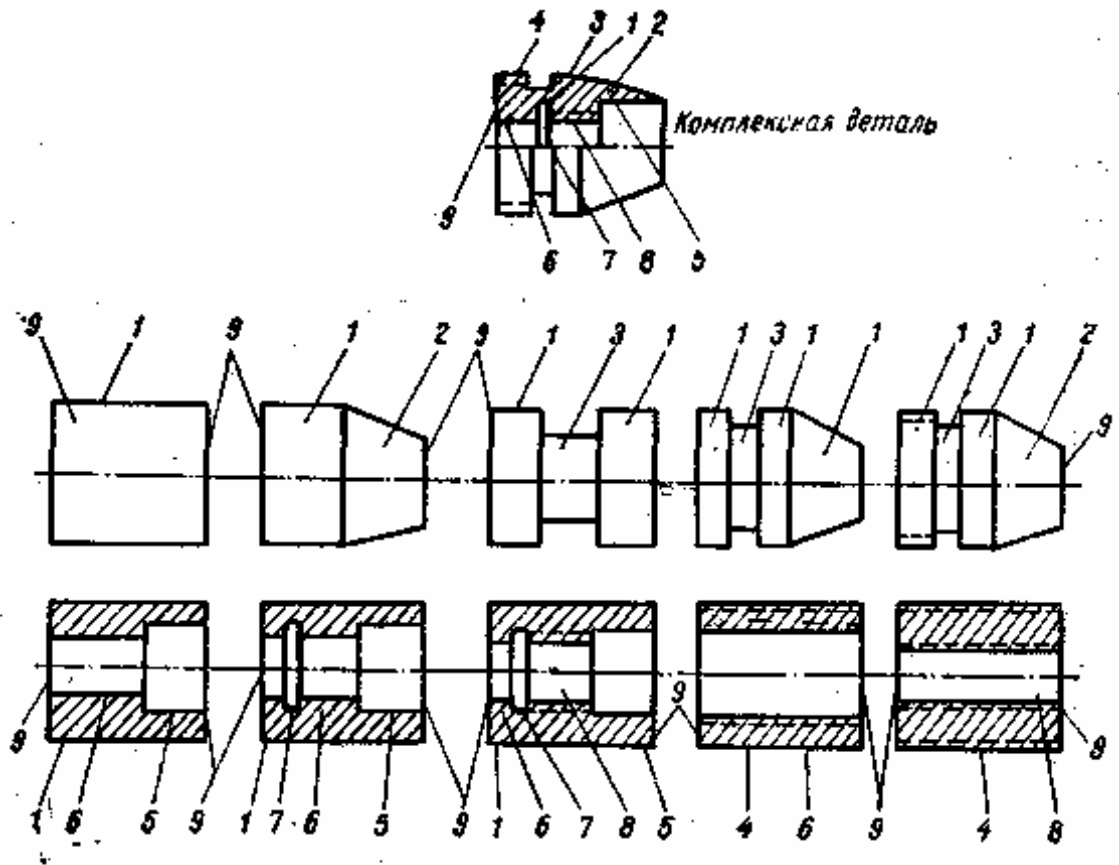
Группа деталей, обрабатываемых при однотипной настройке станка.
